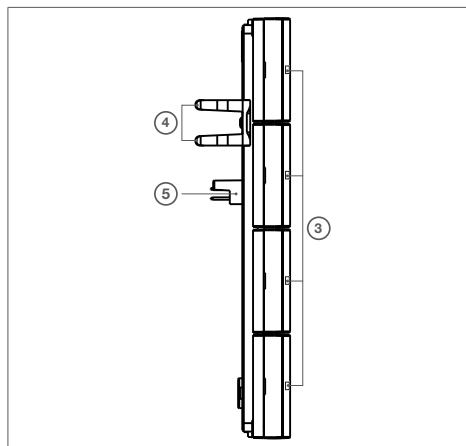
Vue de profil du bloc bouton poussoir 8 touches
